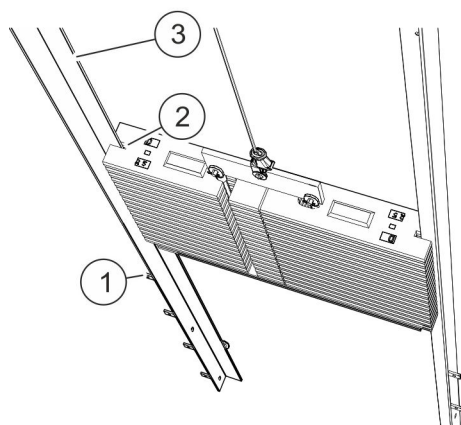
Gleitwinkel der Gewichts-führung im Tunnel
